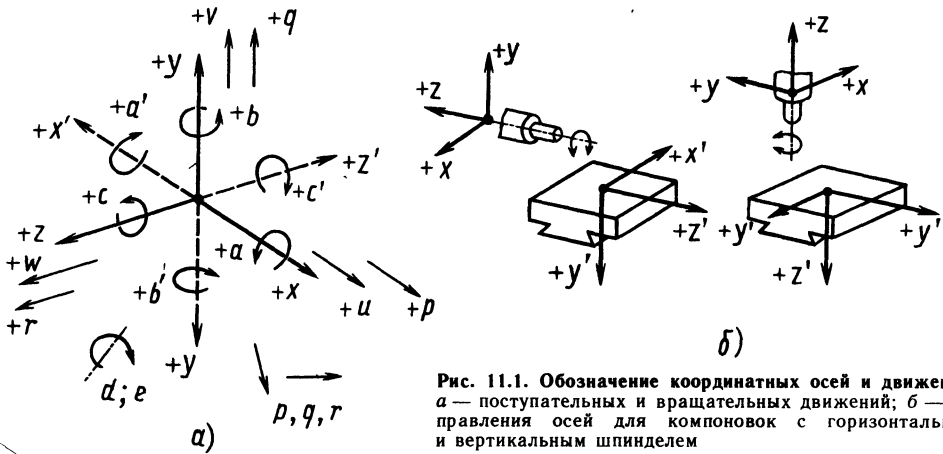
Обозначение координатных осей и движений: *a* — поступательных и вращательных движений; *б* — направления осей для компоновок с горизонтальным и вертикальным шпинделем
